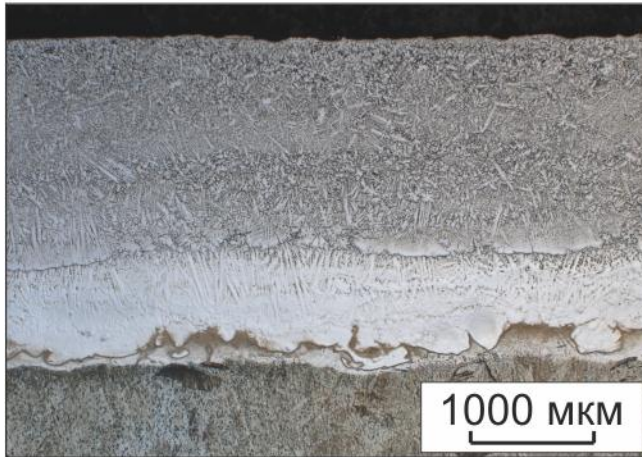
Поперечное сечение титановой заготовки с двукратно наплавленным слоем
